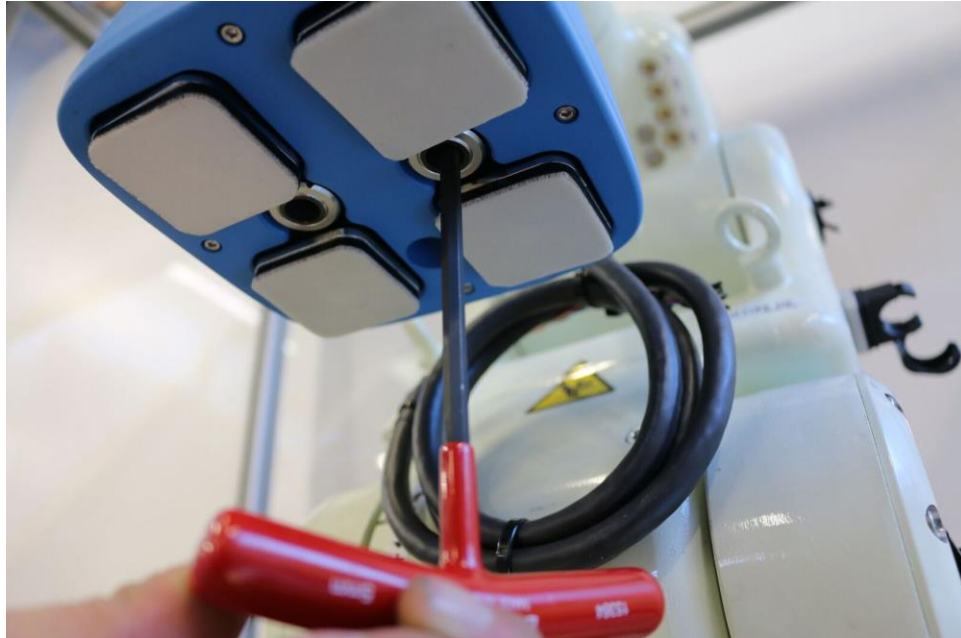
Placa de montaje para robots que no son de Universal Robots.
